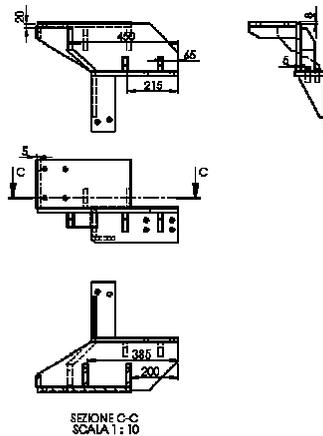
Dispositivi di attacco: quote di assemblaggio per il componente lato sinistro.
